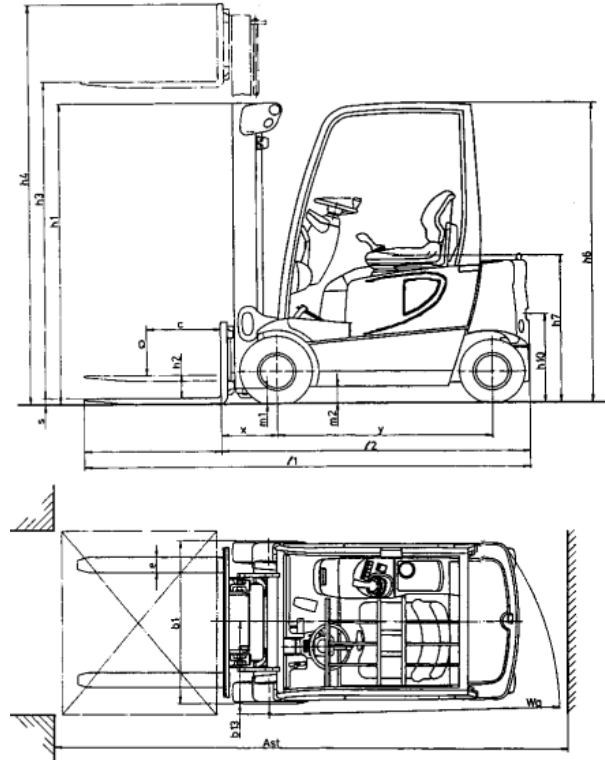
135: Dimensiones – Carretilla elevadora EFG 318.
